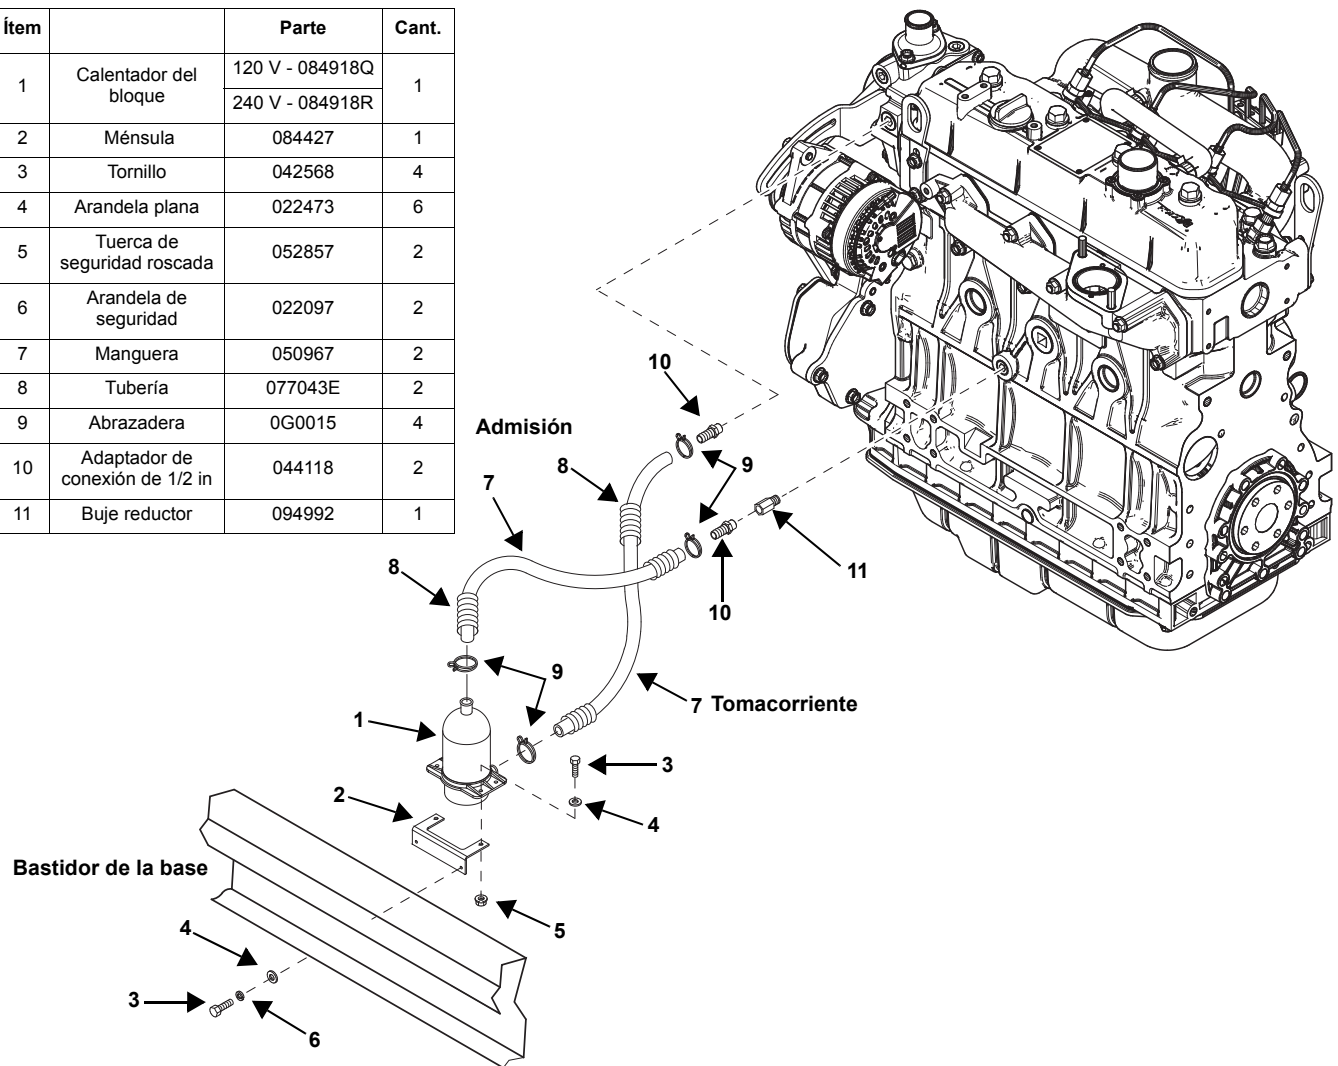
Conjunto de calentador de bloque (despiece, modelos de 2.3 I)
